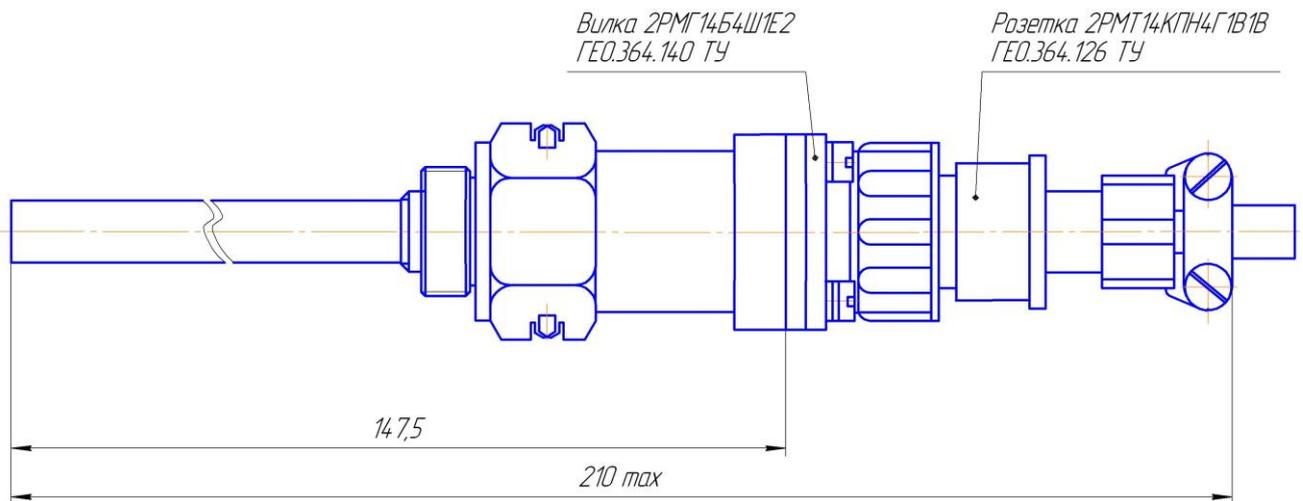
Габаритный чертеж приемника П-1.01 (МКСН.405219.023-01)
